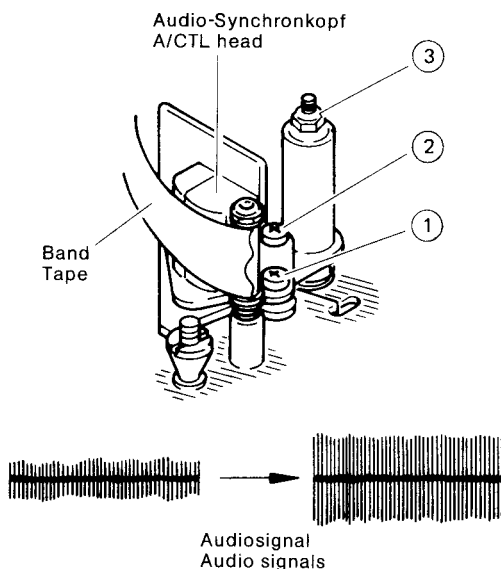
Einstellung des Audio-Synchronkopfes / Audio/Control head adjustment
